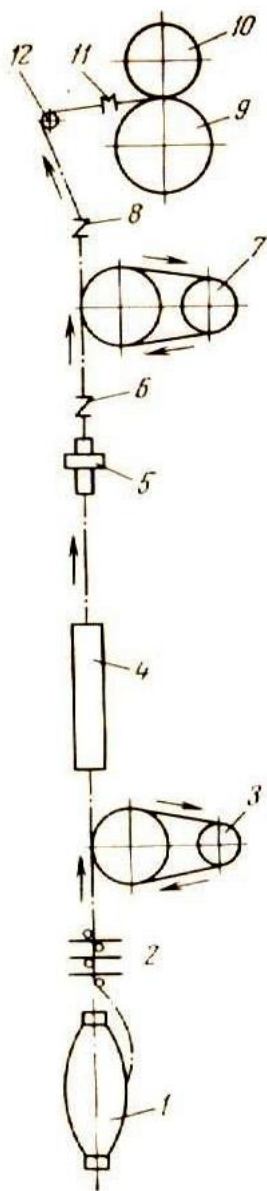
Схема однопроцесного способу виготовлення високорозтяжної нитки
